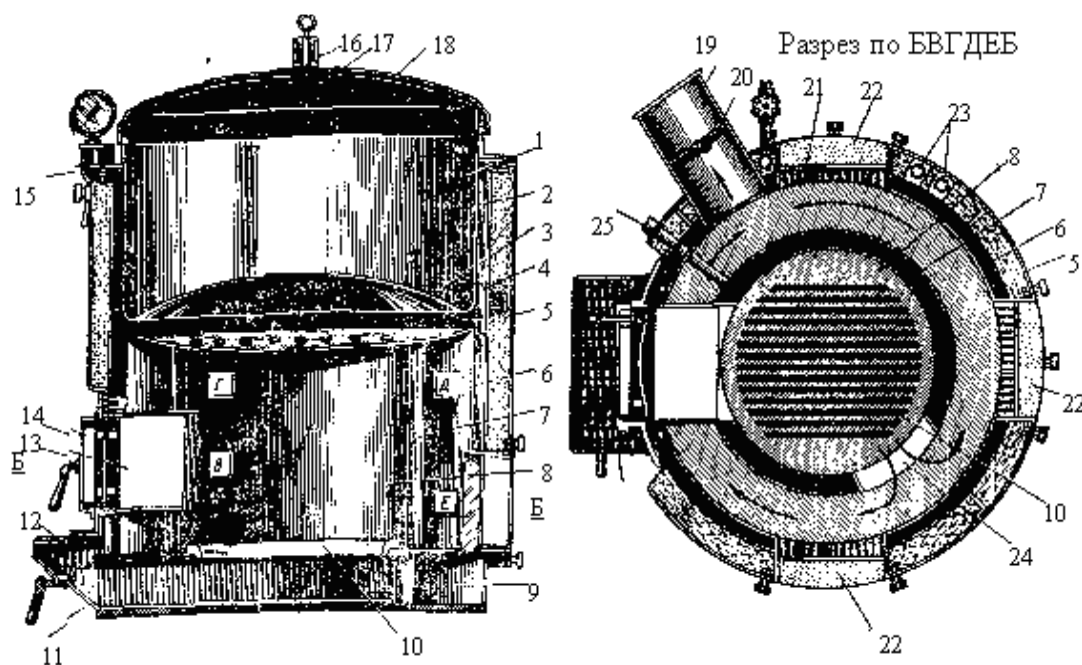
Котел пищеварочный твердотопливный КПТ-160:
